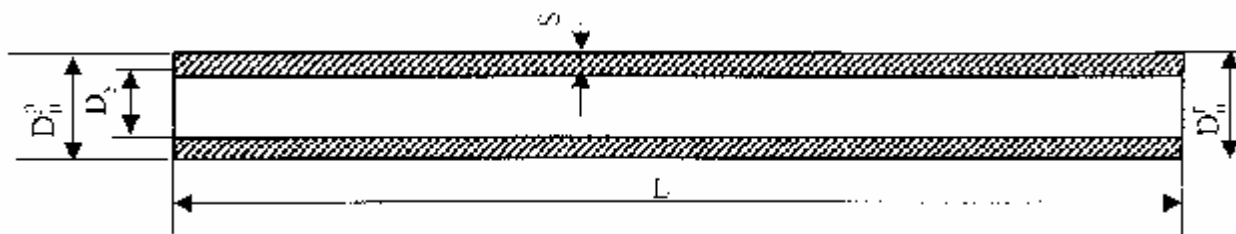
П12. Схема трубы с гладкими концами под сварку (тип А)
